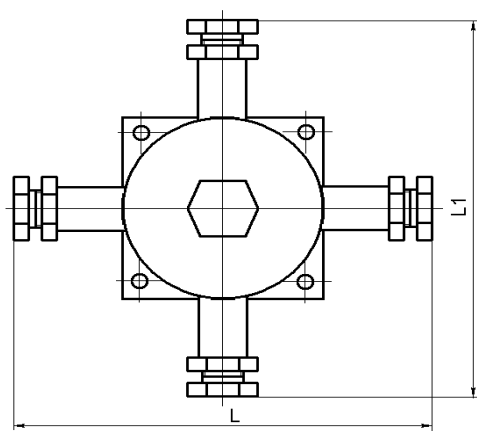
Габаритные, установочные и присоединительные размеры базового варианта коробки ЕхКСУВ (тип 1).
